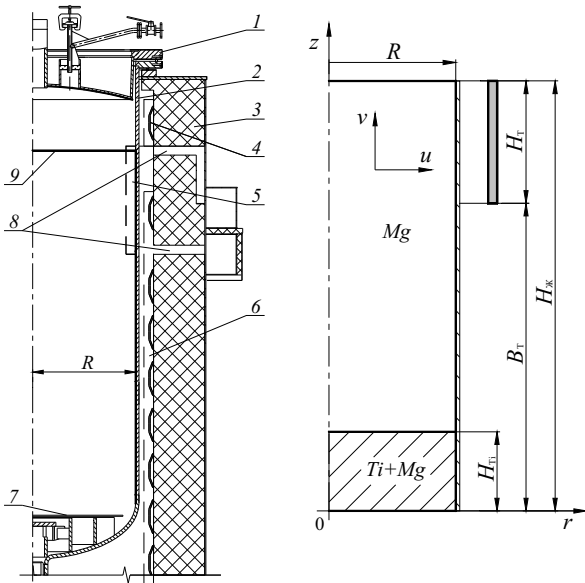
Общий вид аппарата и печи восстановления (слева): 1 – крышка, 2 – реторта, 3 – шахтная электропечь, 4 – верхний нагреватель, 5 – теплообменник, 6 – нижний нагреватель, 7 – решетка эллиптического дна, 8 – каналы печи для подачи и отвода охлаждающего воздуха, 9 – уровень расплава магния в реторте.
